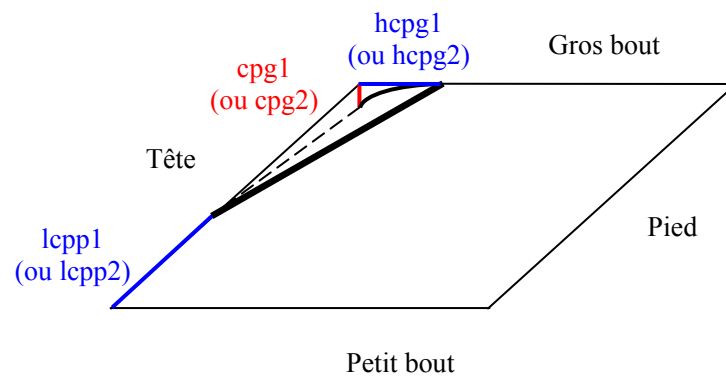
Correction de profil sur le pignon (ou sur la roue) sur le gros bout seulement
